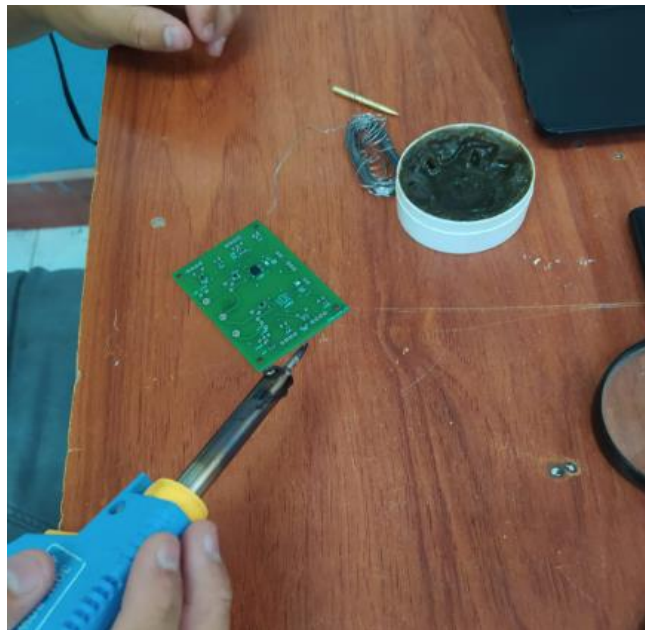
Soldadura de componentes SMD en tarjeta PCB.
